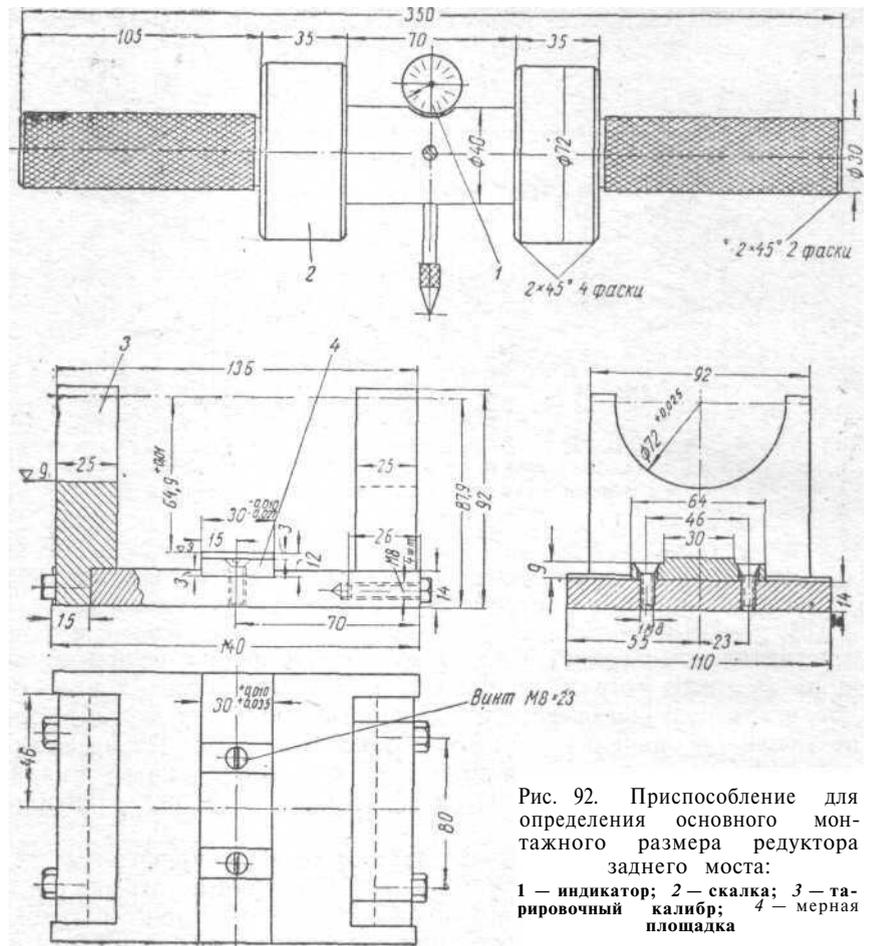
Приспособление для определения основного монтажного размера редуктора заднего моста:
